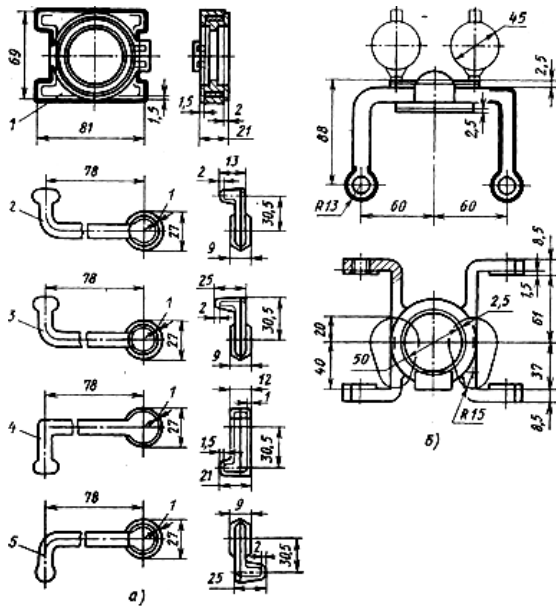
Изготовление детали из пяти заготовок (1-5): а – их сваркой (применяемая технология); б – отливка детали по выплавляемым моделям
